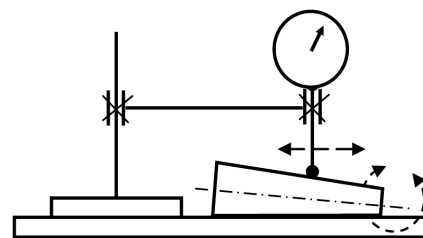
Схема измерительного контроля параметра номинально цилиндрической детали
